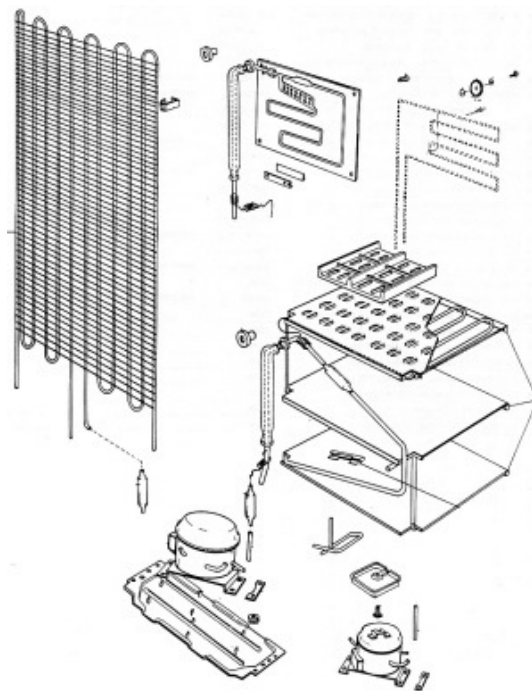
Despiece explosivo componentes fluidos refrigerantes y aceites.
